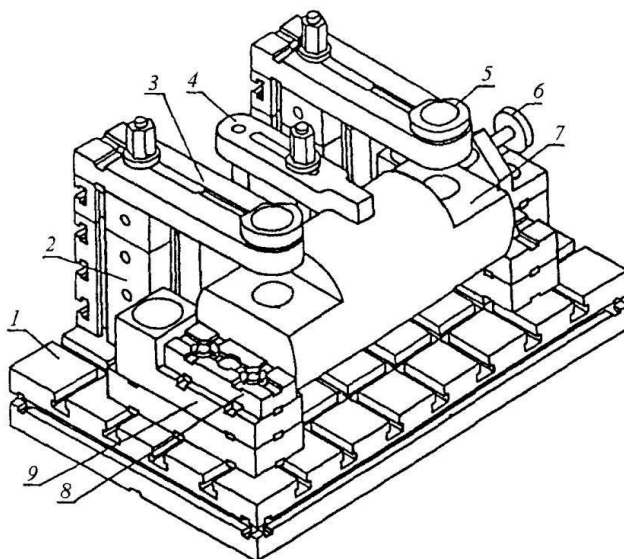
Кондуктор из УСП для сверления 2-х отверстий:
